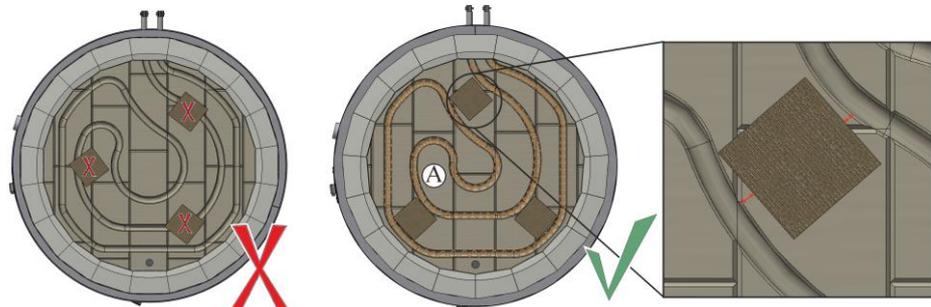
Exemple : Disposition des plaques de montage (accessoires) (figure similaire)
